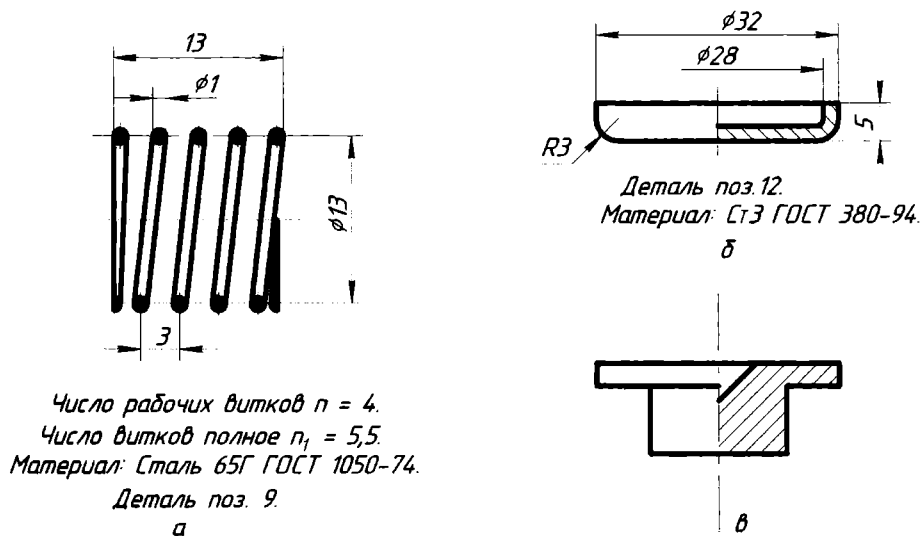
Чертежи: а — пружины; б — тарелки; в — упора
